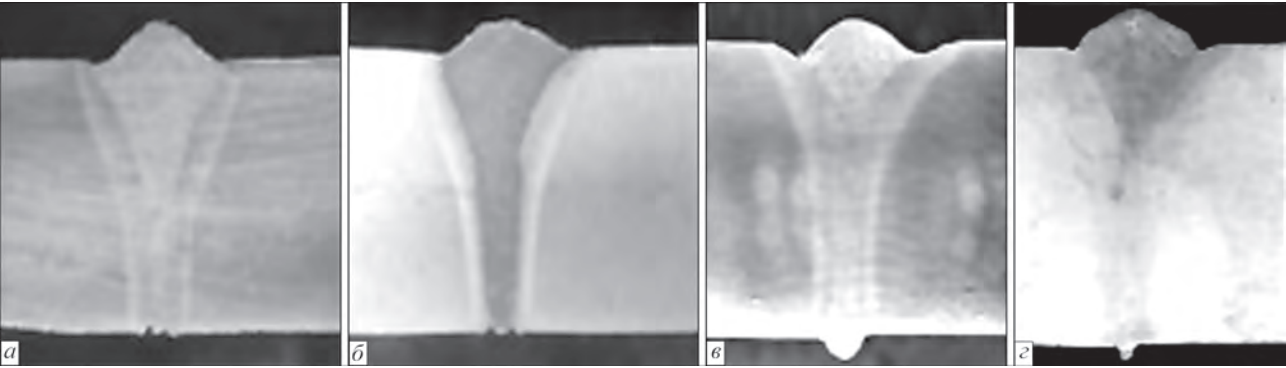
Типичные дефекты формирования стыковых соединений высокопрочной стали DOMEX 390 XR ($\delta = 10$ мм) при гибридной лазер-MIG сварке [6]: утягивание корня шва (*a, б*), подрезы в верхней части (*a–г*)
